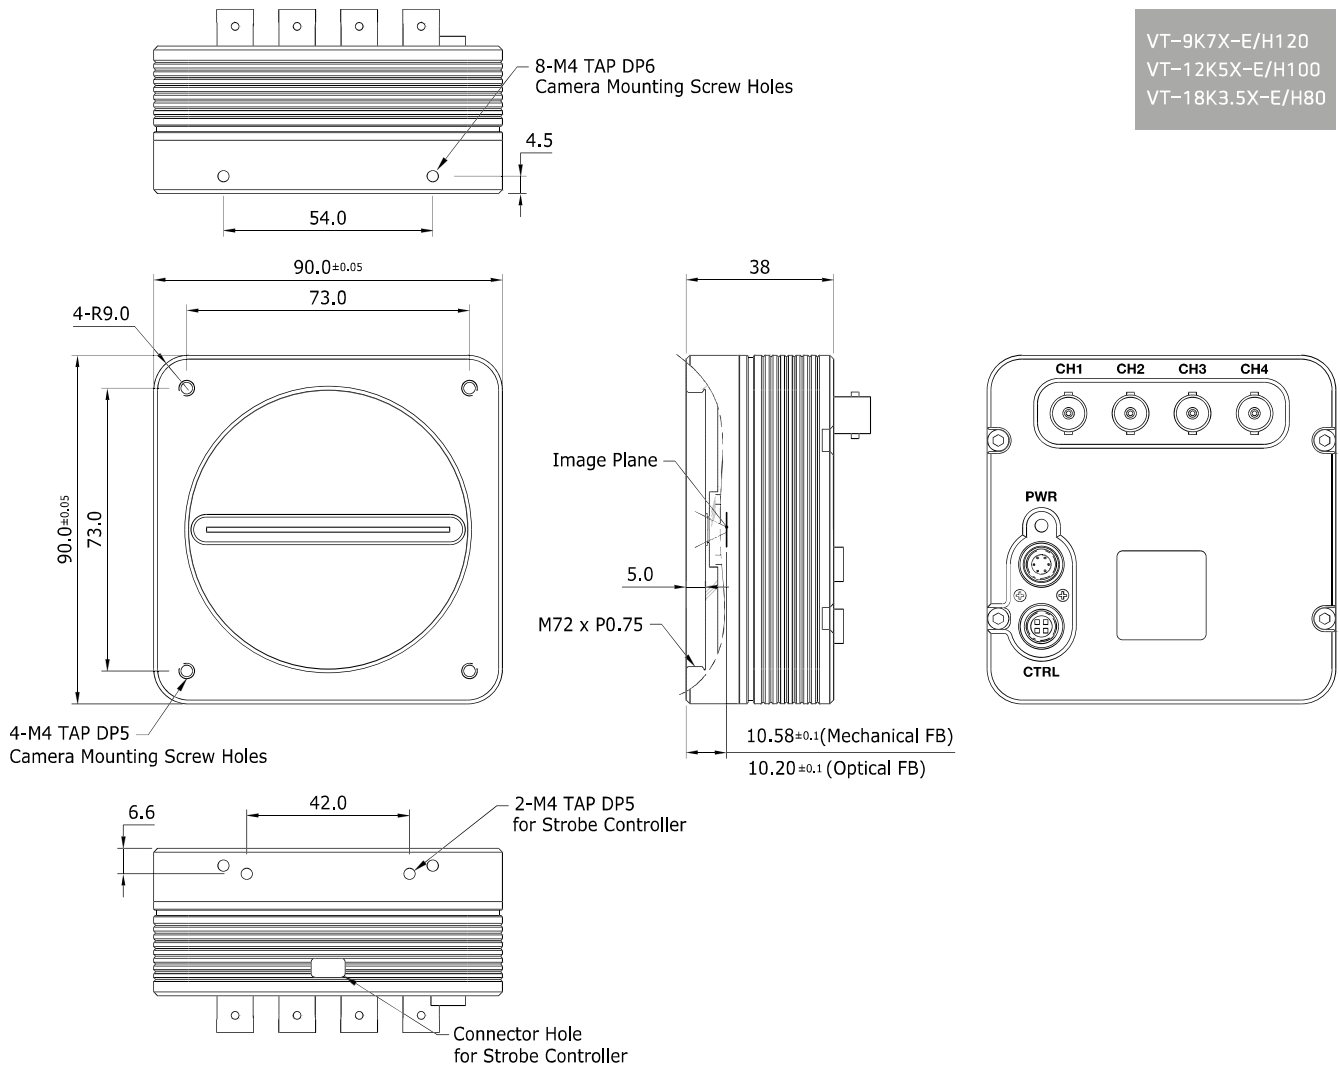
M72 mount 지원 VT CXP Series Mechanical Dimension(계속)
